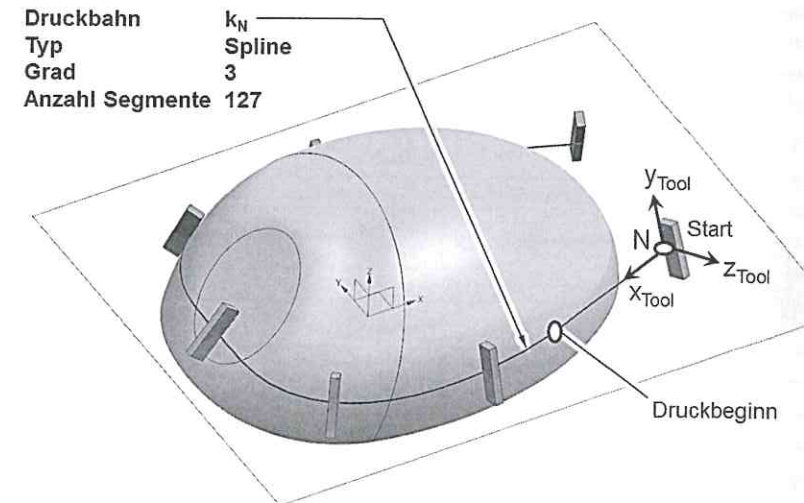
Kappenförmiges Druckobjekt mit beispielhafter Toolbewegung.
